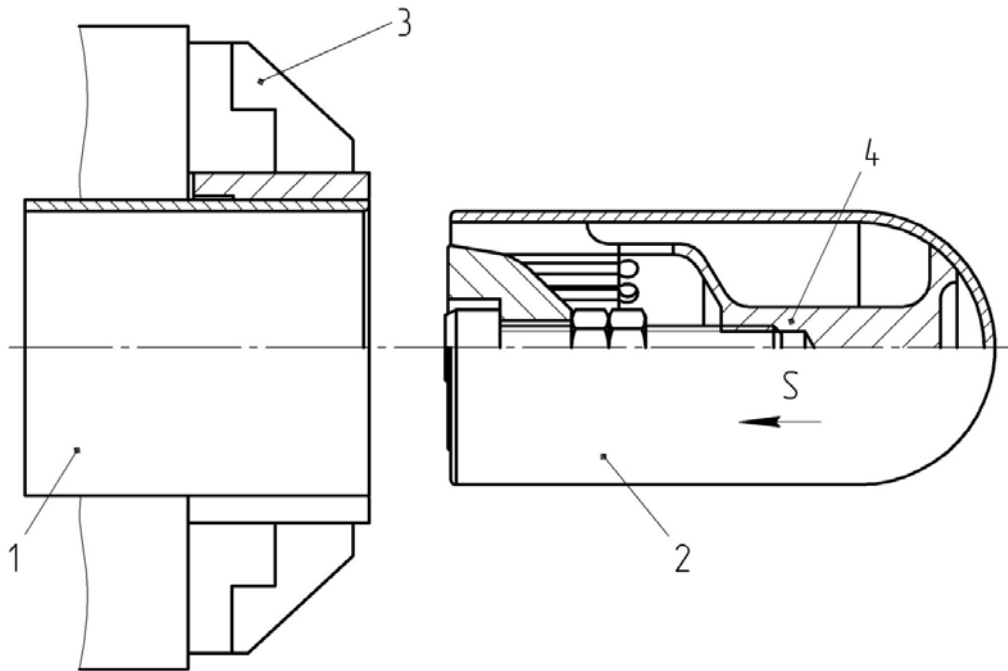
Установка детали 1 в приспособлении с широкими кулачками 3
